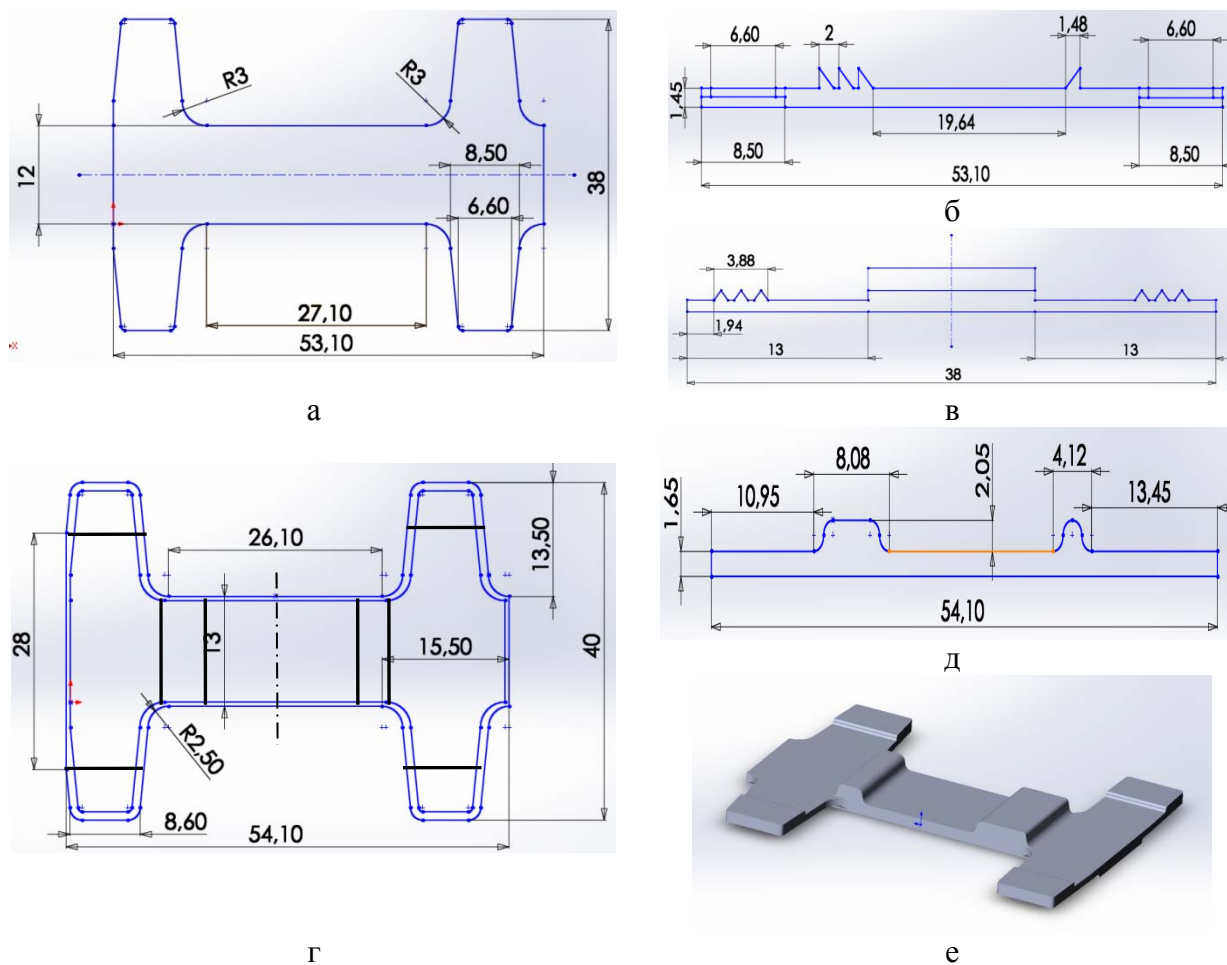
Развёртка детали (а–в) и поковки (г, д) с размерами:
